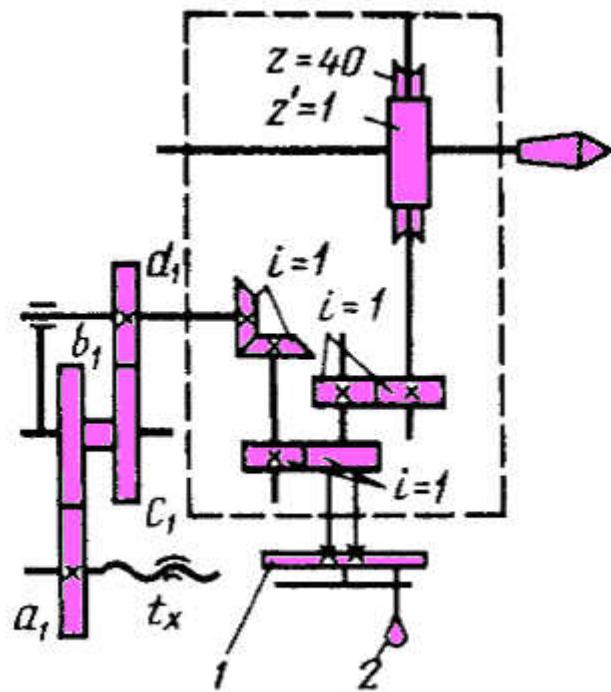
Схема делительной головки настроенной на фрезерование спиральных винтовых канавок: 1-делительный диск; 2- рукоятка; 3- шпиндель головки; z^u - число заходов червяка; $z=40$ - число зубьев червячного колеса; a,b,c,d- гитара сменных колес
